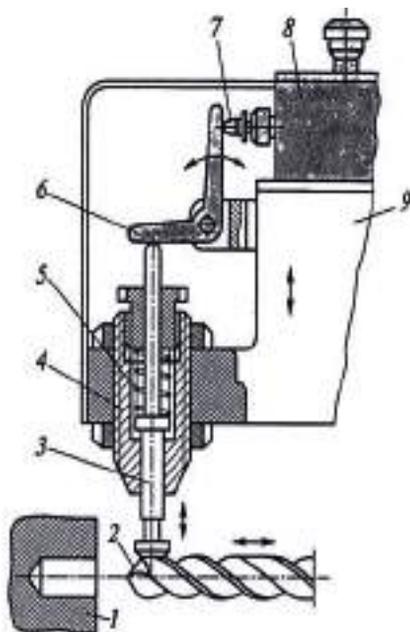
Контрольно-блокировочное устройство автомата для проверки целостности осевого инструмента: 1 – заготовка; 2 – сверло; 3 – щуп; 4 – втулка; 5 – пружина; 6 – рычаг; 7 – измерительный стержень; 8 – электроконтактный преобразователь; 9 – корпус
